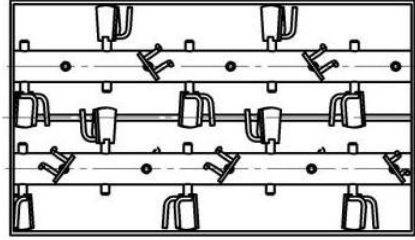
Схема рабочей камеры смесителя со стержневыми элементами
